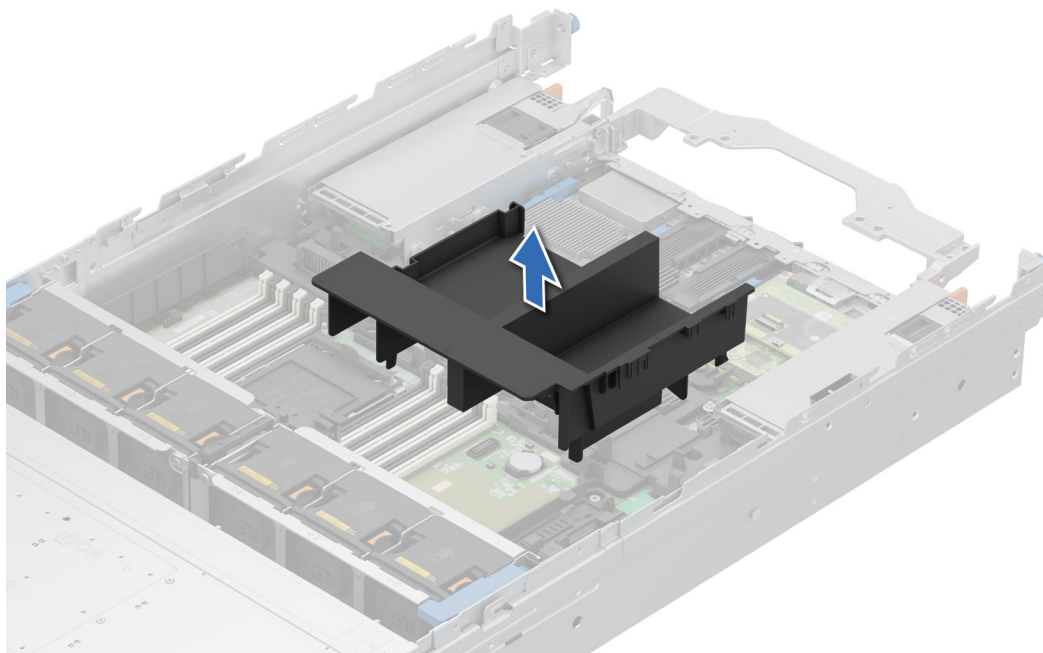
Extracción de la cubierta para flujo de aire derecha
